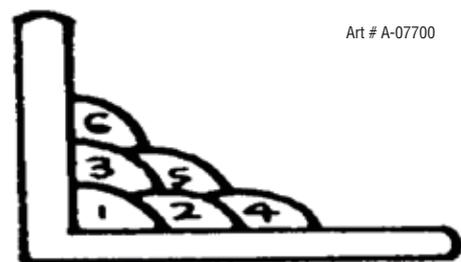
Plusieurs cordons dans la soudure du joint HV
